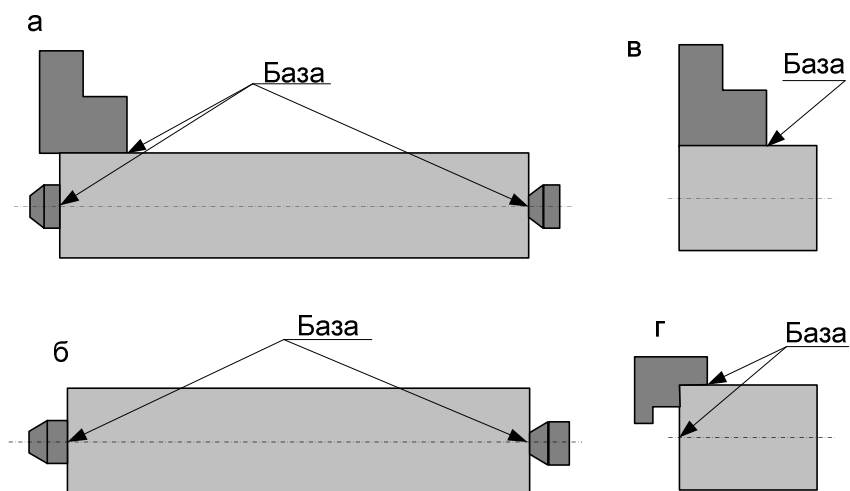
Технологические базы при способах установки заготовок на токарном станке: а – в патроне и заднем центре с опорой на шпиндельный упор; б – в центрах; в – в патроне; г – в обратных кулачках патрона.
